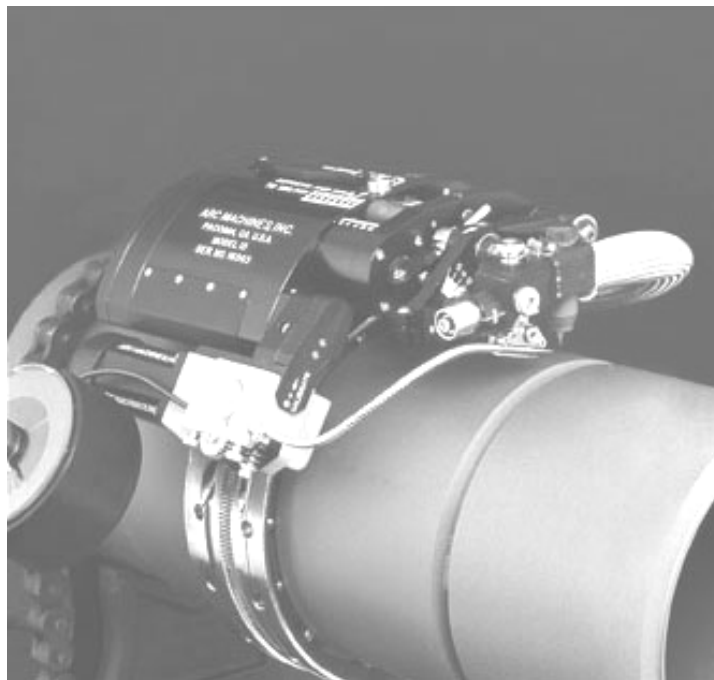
美国 AMI 公司研制的 Model 15 Large-Diameter Pipe Weld Head
